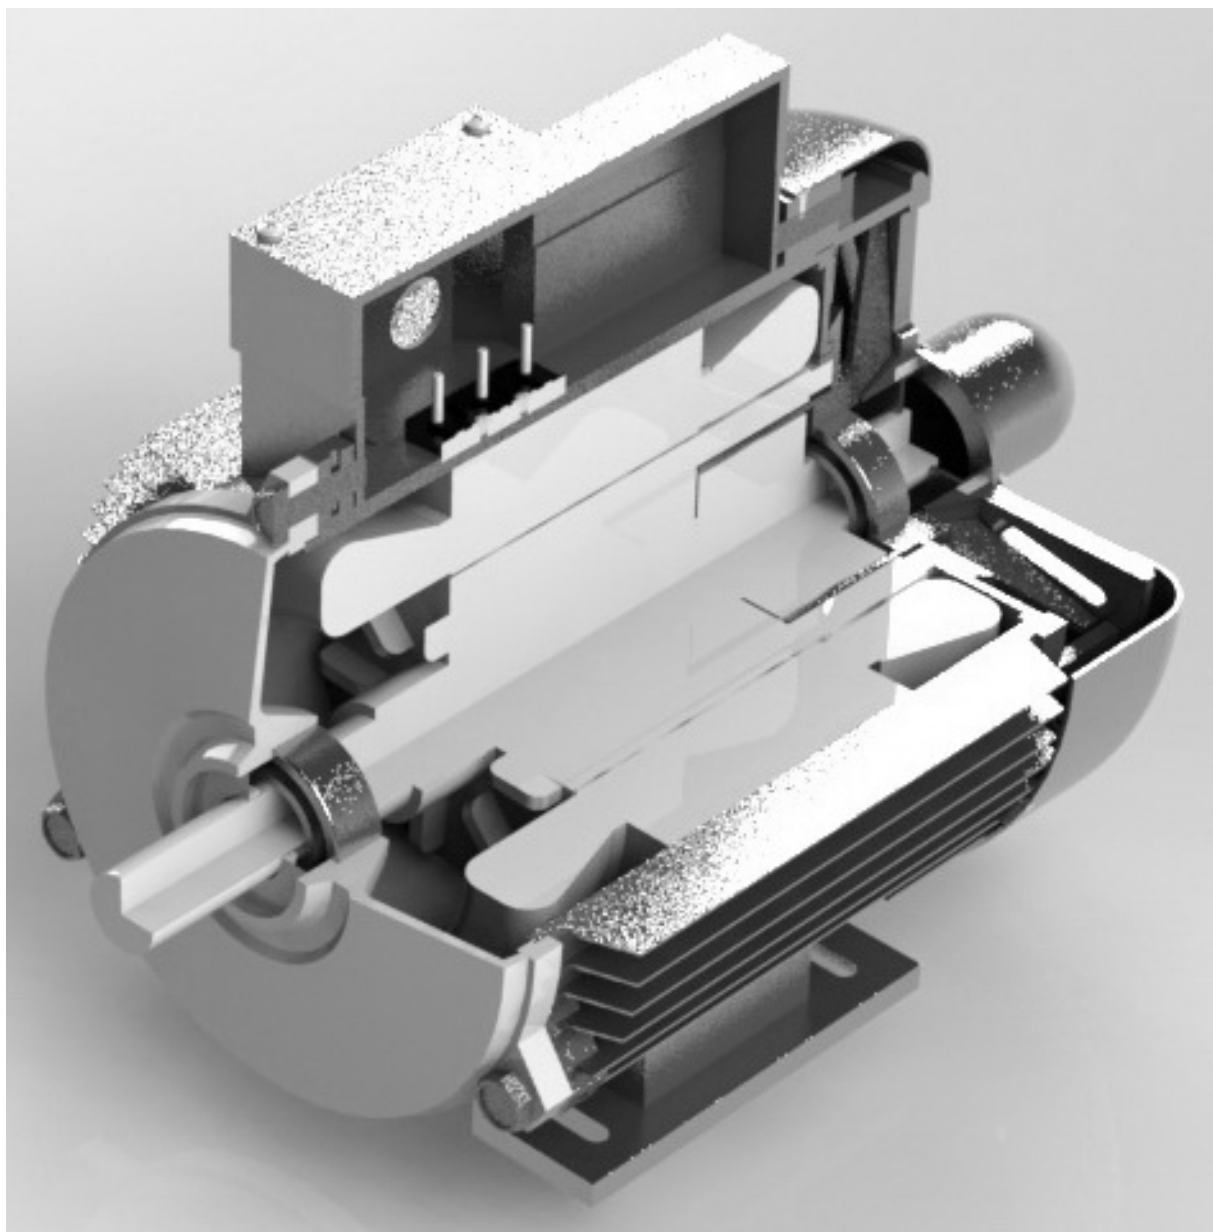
Внешний вид энергоэффективного двигателя улучшенной конструкции
